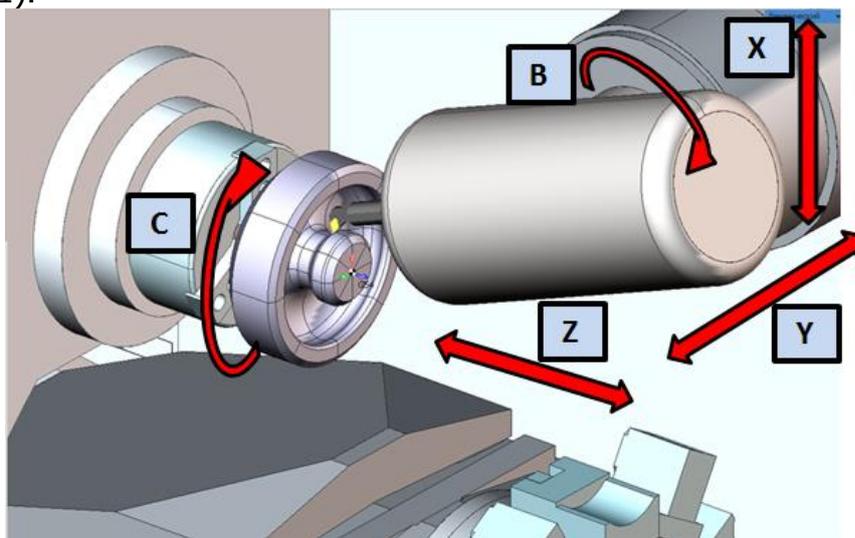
Кинематическая схема 5-ти координатного токарно-фрезерного ОЦ
